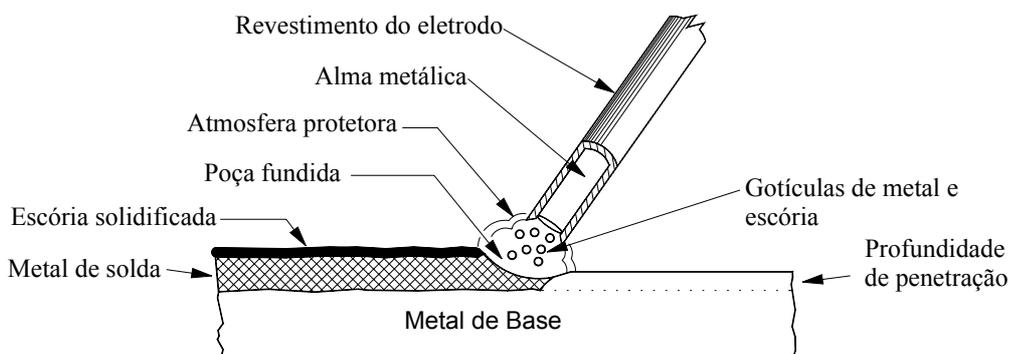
Processo de soldagem com Eletrodo Revestido.
